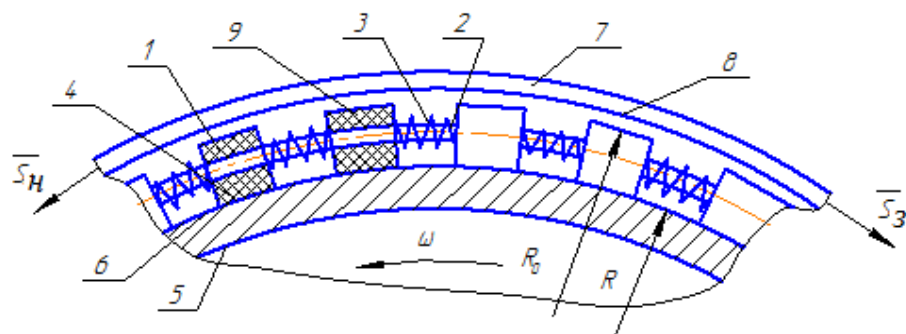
Схема фрикційного вузла стрічково-колодкового гальма з рухомими фрикційними накладками: 1, 4, 9 – фрикційна накладка з внутрішньою і зовнішньою поверхнями; 2, 3 – циліндричні стрижні та пружини; 5, 6 – гальмовий шків і його робоча поверхня; 7, 8 – гальмова стрічка з робочою поверхнею
